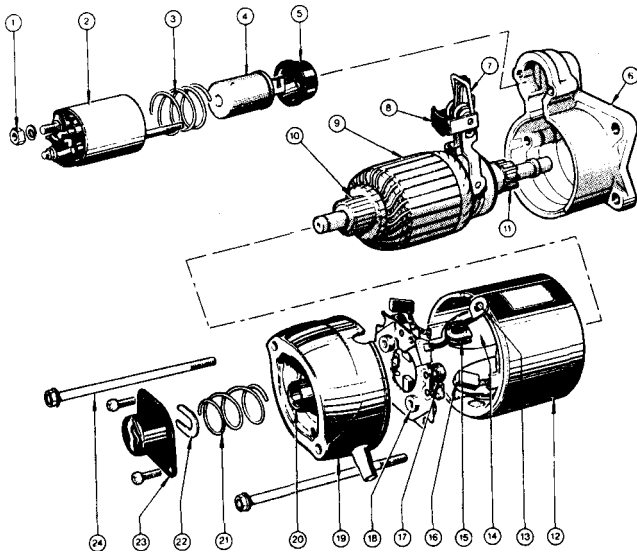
Разобранный стартер NIPPONDENSO. 1 - Гайка клеммы. 2 - Корпус реле. 3 - Пружина. 4 - Якорь. 5 - Уплотнитель. 6 - Крышка со стороны привода. 7 - Пусковой рычаг. 8 - Ось поворота. 9 - Якорь. 10 - Коллектор. 11 - Агрегат ведущей шестерни и муфты свободного хода. 12 - Основной корпус. 13 - Соединительное звено. 14 - Обмотка. 15 - Уплотнитель. 16 - Щетка. 17 - Пружина щетки. 18 - Пластина щеток. 19 - Конечный корпус коммутатора. 20 - Щетка. 21 - Пружина. 22 - С-образное кольцо. 23 - Крышка корпуса привода. 24 - Стяжной болт.
